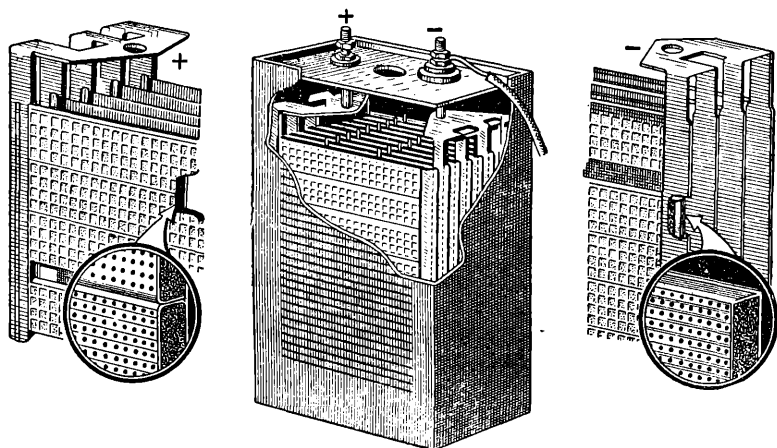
Внешний вид и устройство пластин щелочного аккумулятора.
